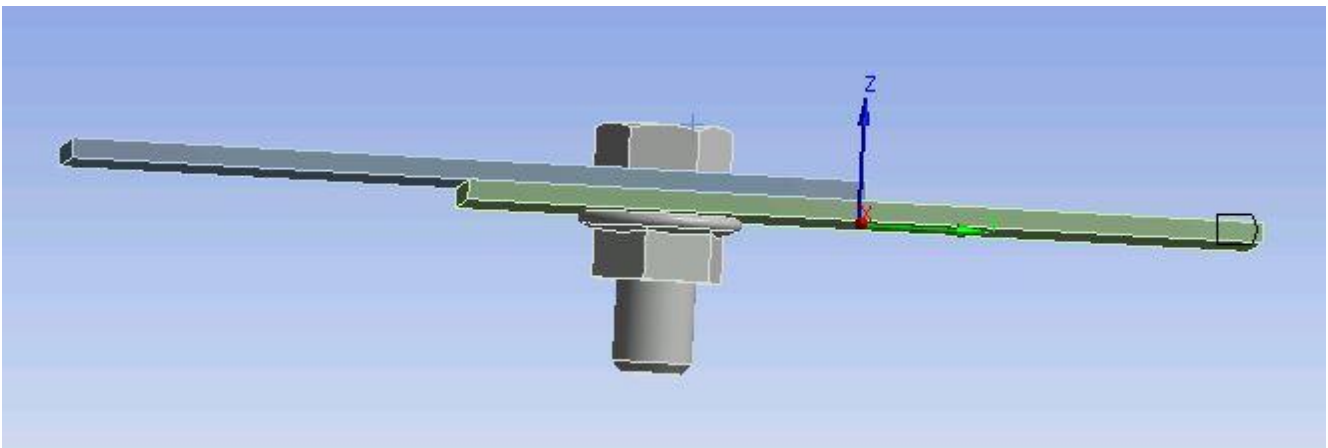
Segunda restricción: desplazamiento en la chapa 2
